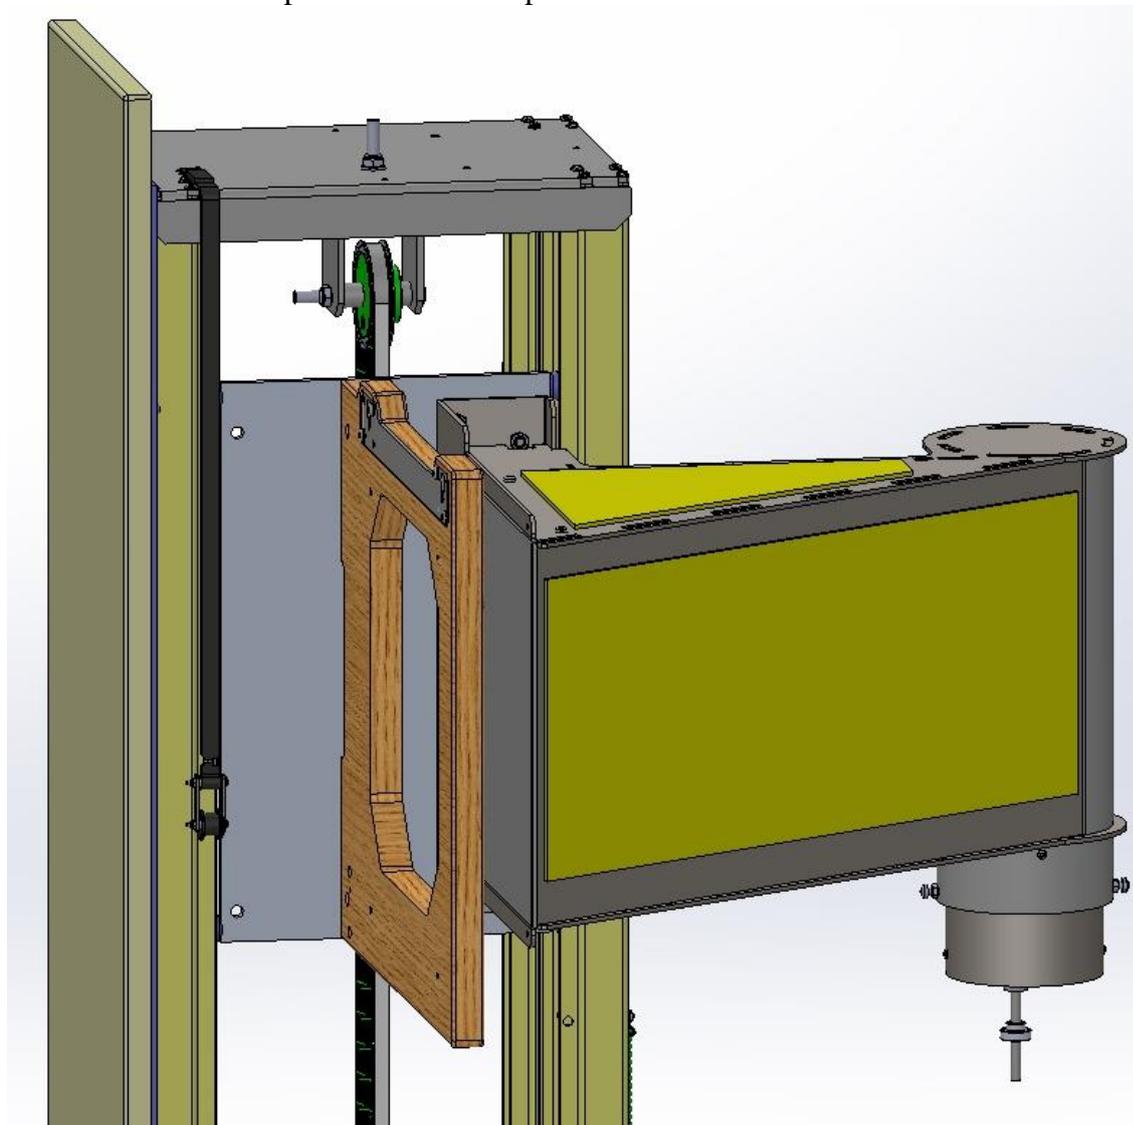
viser feste for skive og stålkulefang. Skru fast disse med medfølgende skruer.
